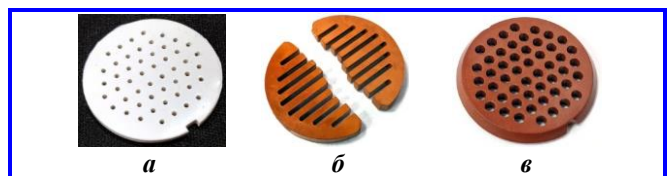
Выбранные составные части соединителя РС50: а – резиновая уплотнительная прокладка вилки; б – решетка из пресс-материала; в – сепаратор
